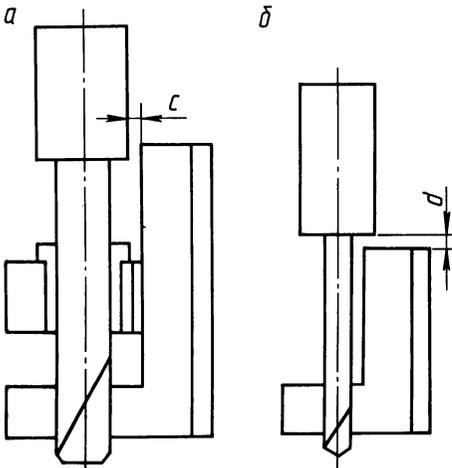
Расположение вспомогательного инструмента относительно обрабатываемой детали.
